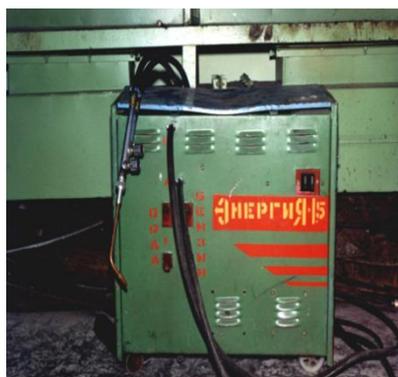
Установка сварочная водородно-кислородная Энергия-1,5
